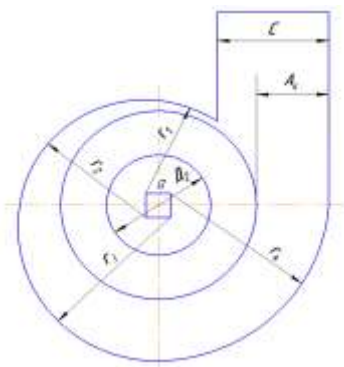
Корпус вентилятора: C – высота выпускного окна; A_k – разворот спирали корпуса; D_2 – наружный диаметр ротора; a – размер конструкторского квадрата; r_1, r_2, r_3, r_4 – радиусы обечайки корпуса
